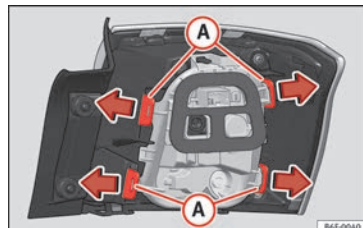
Befestigungsglaschen Rückseite Heckleuchte.
